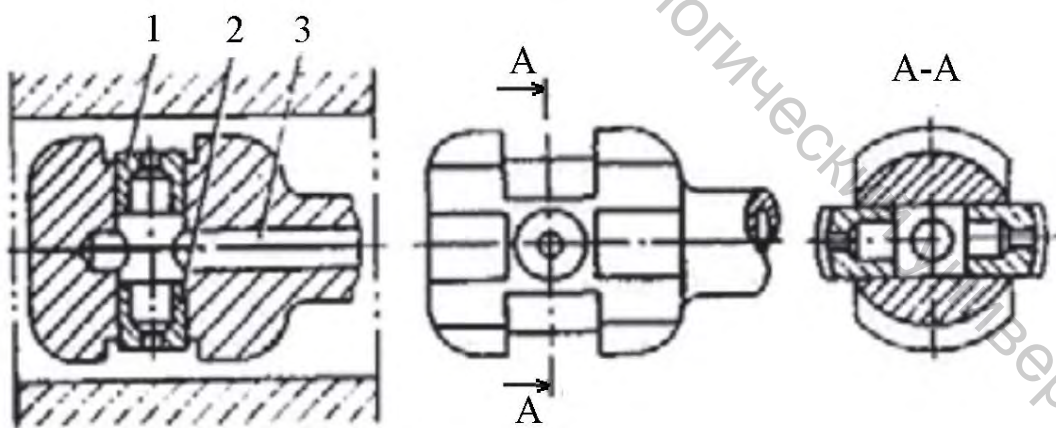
Пробка для контроля глубоких отверстий:
